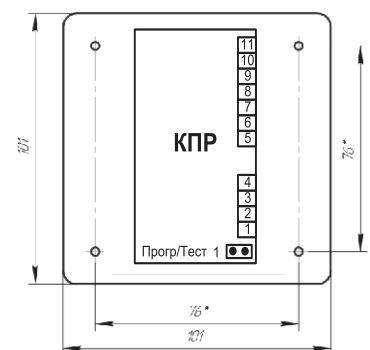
Габаритные размеры контроллера считывателя карт Proximity.
